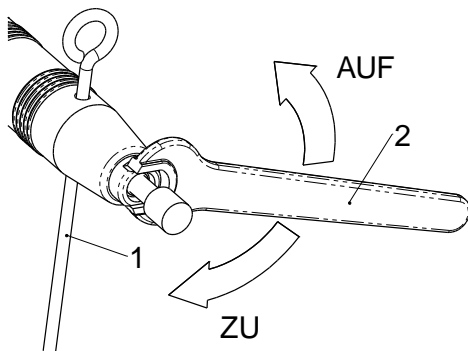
Werkzeugwechsel Spannzange ZG 1/6
